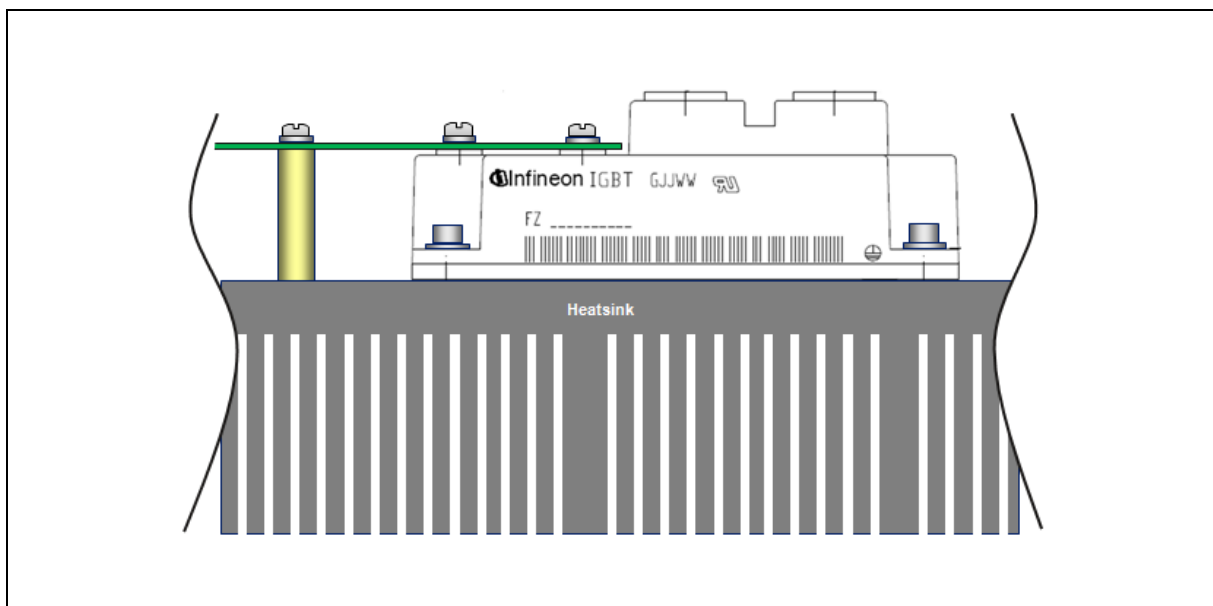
Beispiel Montage der Steuerkontakte bei Verwendung einer Ansteuerbaugruppe auf dem Modul
